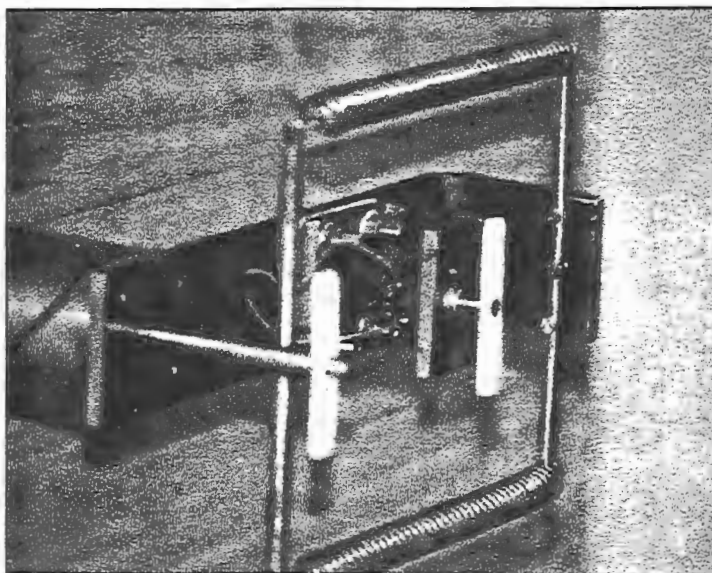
Detalhe do conjunto de molas de oscilação.
